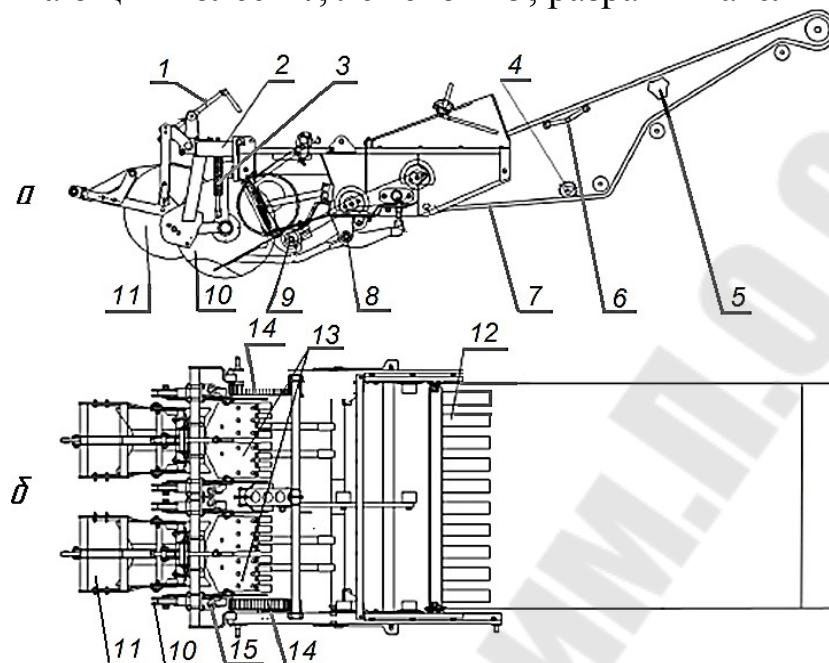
Блок подкапывающе-сепарирующий и первый сепарирующий транспортер: *а* – вид сбоку, *б* – вид сверху; 1 – механизм установки глубины подкапывания пласта; 2 – рама; 3 – механизм установки глубины хода подрезающих дисков; 4 – валец, очищающий транспортер; 5, 6 – встряхиватели пассивные; 7 – элеватор первый сепарирующий; 8 – балка лемехов; 9 – валец ребристый; 10 – диски подрезающие; 11 – катки копирующие; 12 – разравниватель почвы; 13 – лемеха; 14 – колеса ботвоподтягивающие; 15 – механизм регулирования усилия прижатия ботвоподтягивающих колес к транспортеру
